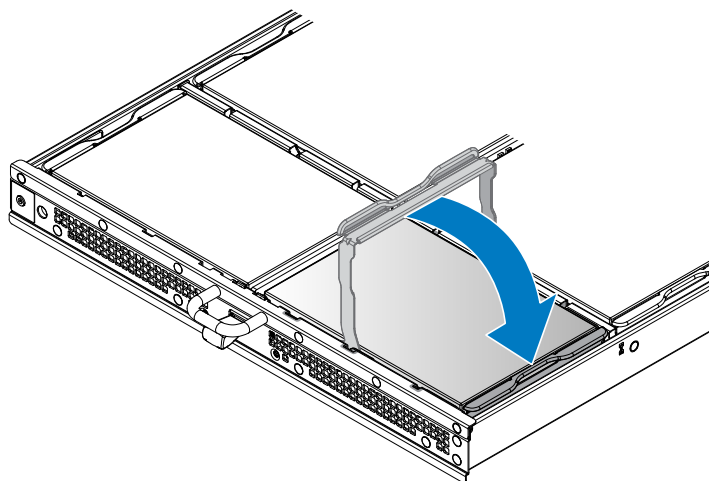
Installation de l'assemblage de disque dur de 3,5 pouces
